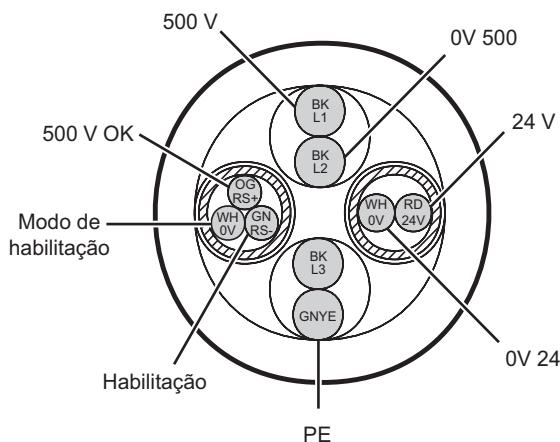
Corte transversal do cabo híbrido pré-fabricado
